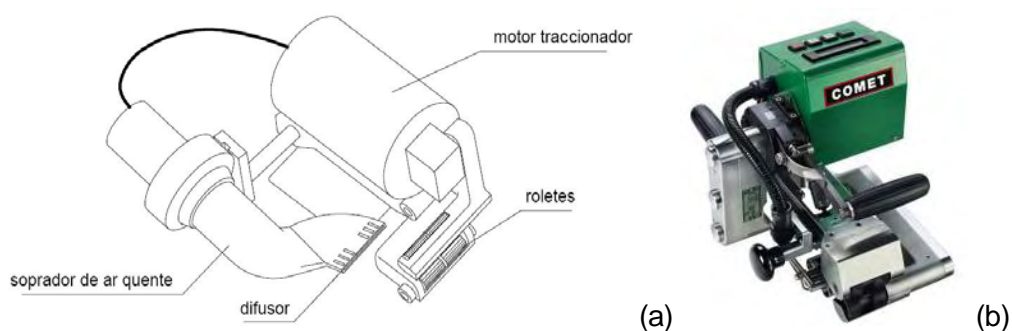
Representação esquemática de uma máquina de soldadura dupla (a) e imagem real da mesma (b).
